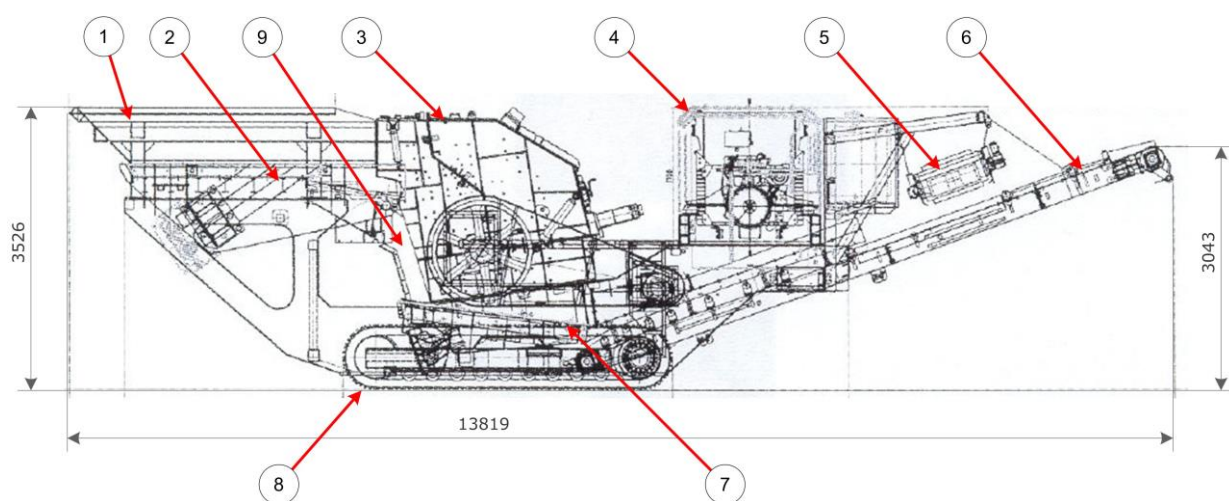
Схематический чертеж установки Gіporec R 130 C
